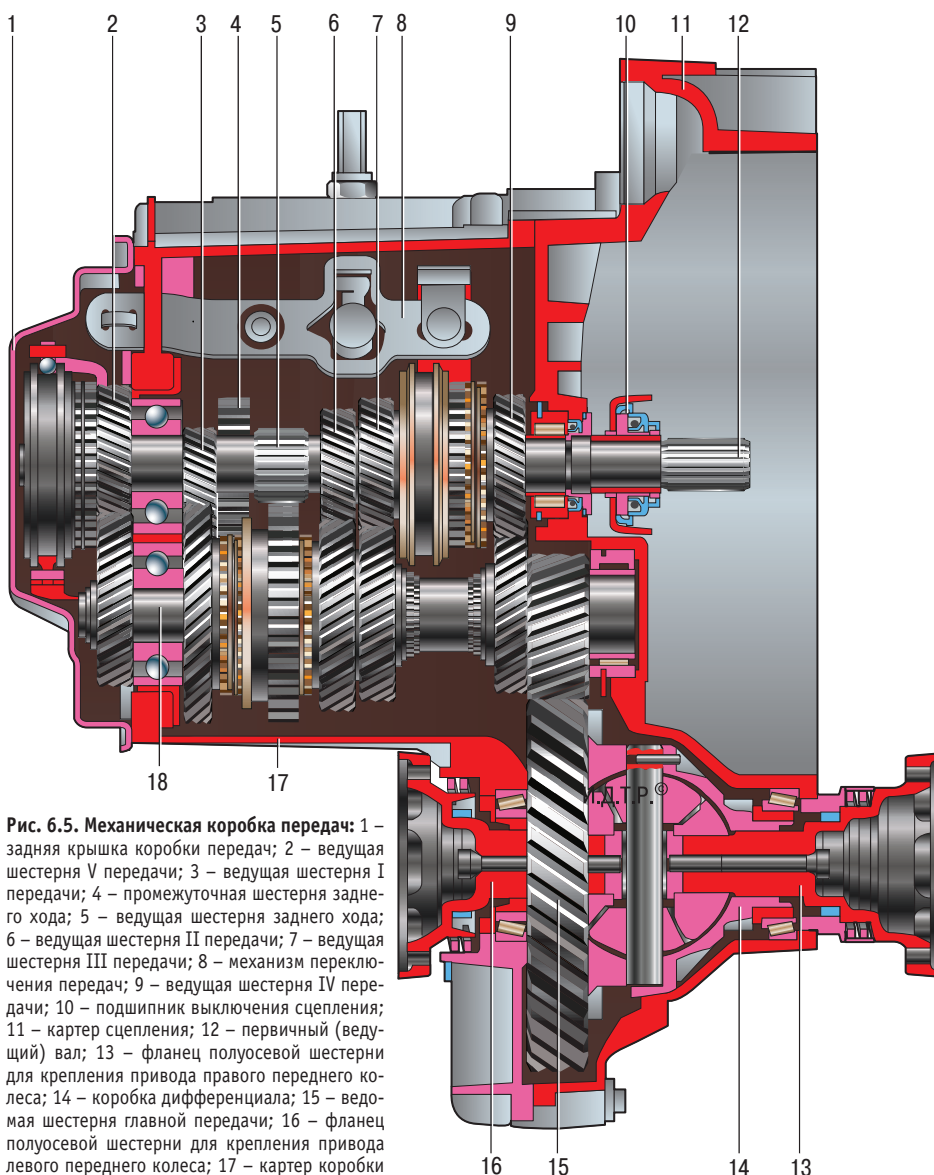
Механическая коробка передач: 1 – задняя крышка коробки передач; 2 – ведущая шестерня V передачи; 3 – ведущая шестерня I передачи; 4 – промежуточная шестерня заднего хода; 5 – ведущая шестерня заднего хода; 6 – ведущая шестерня II передачи; 7 – ведущая шестерня III передачи; 8 – механизм переключения передач; 9 – ведущая шестерня IV передачи; 10 – подшипник выключения сцепления; 11 – картер сцепления; 12 – первичный (ведущий) вал; 13 – фланец полуосевой шестерни для крепления привода правого переднего колеса; 14 – коробка дифференциала; 15 – ведомая шестерня главной передачи; 16 – фланец полуосевой шестерни для крепления привода левого переднего колеса; 17 – картер коробки передач; 18 – вторичный (ведомый) вал
